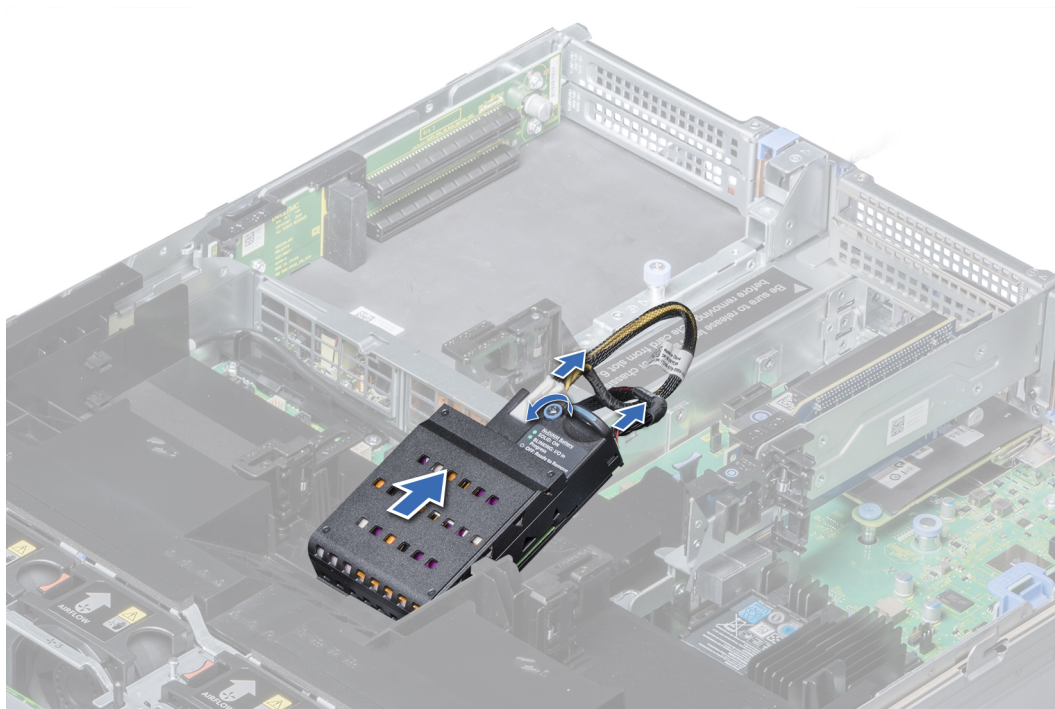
Entfernen der NVDIMM-N-Batterie aus dem Kühlgehäuse
